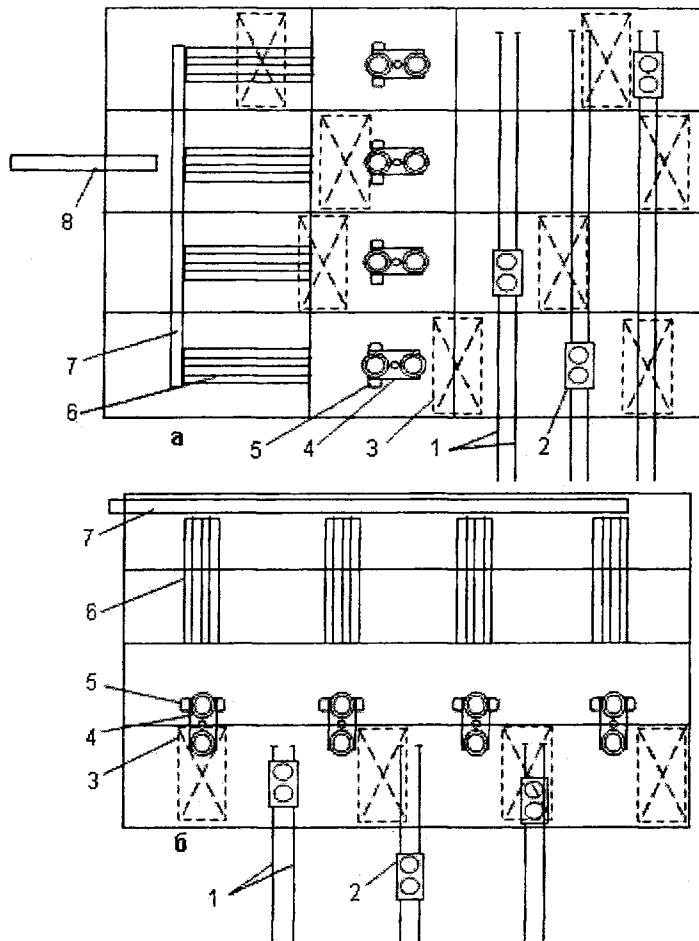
Схемы объёмно-планировочного решения ОНРС с блочным (а) и линейным (б) расположением МНЛЗ: 1 – сталевозные пути; 2 – сталевоз; 3 – разливочный кран; 4 – поворотный стенд МНЛЗ; 5 – промежуточный ковш; 6 – ручьи МНЛЗ; 7 – рольганг; 8 – транспортно-отделочная линия
